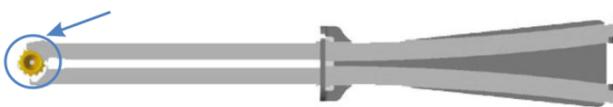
Outil de desserrage des raccords placé sur la denture dynamométrique
